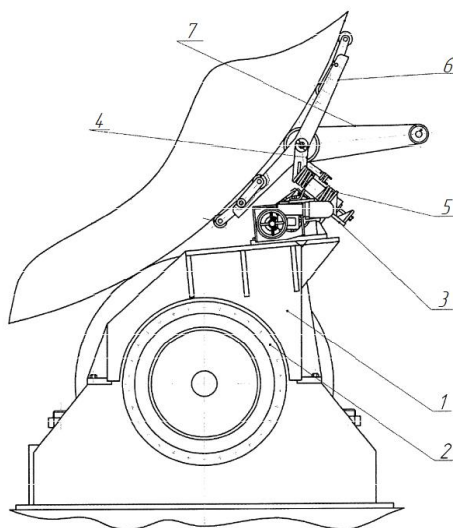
Станок для обработки бандажей: 1- опорные стойки; 2- подшипниковый узел; 3- суппорт; 4- пиноль; 5- пружина; 6- роликовая тележка; 7- абразивная лента [5]
